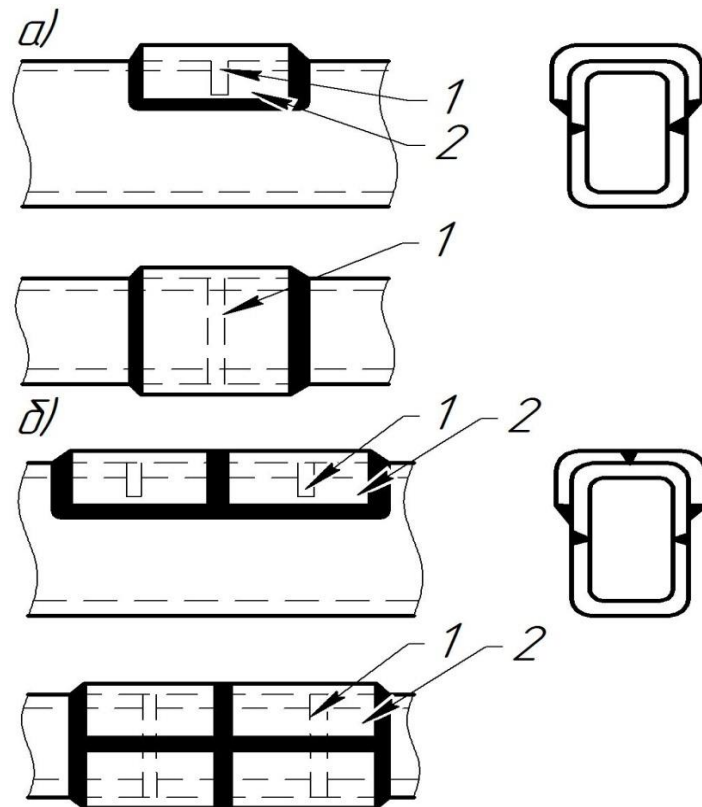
Схеми конструктивних підсилень після зварювання тріщини
